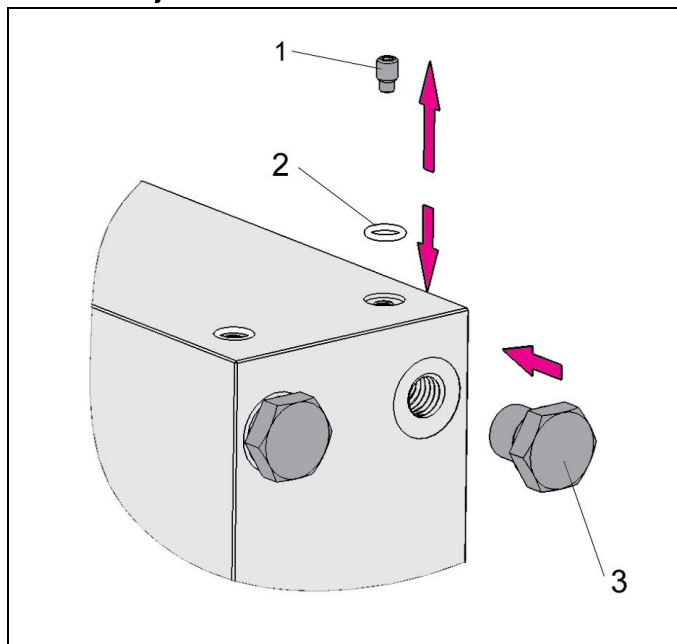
Ejemplo, preparación para el montaje con conexión hidráulica sin tuberías
